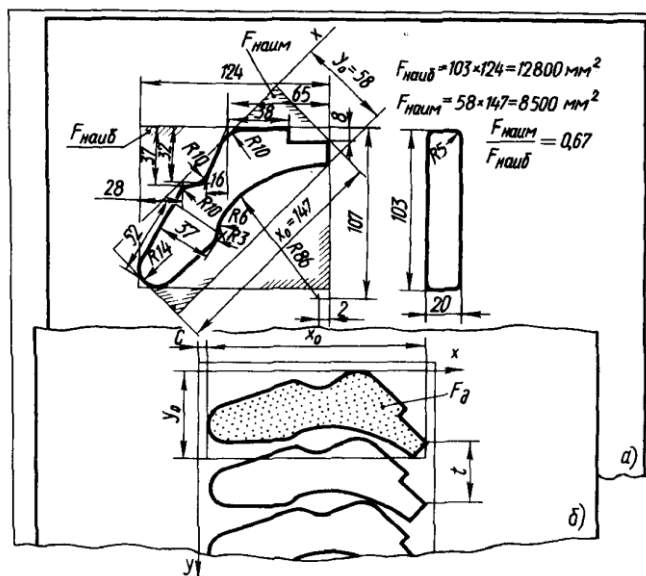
Чертеж плоской детали (а) и карта раскроя (б)
